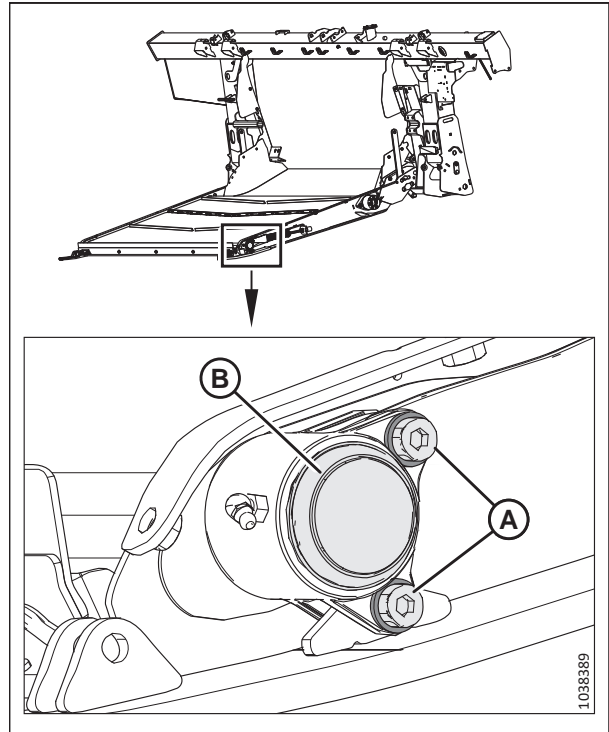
Rodamiento del rodillo tensor izquierdo
